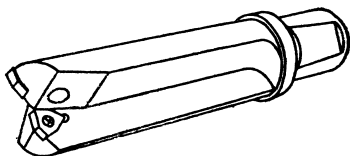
Сверла с механическим креплением твердосплавных пластин
